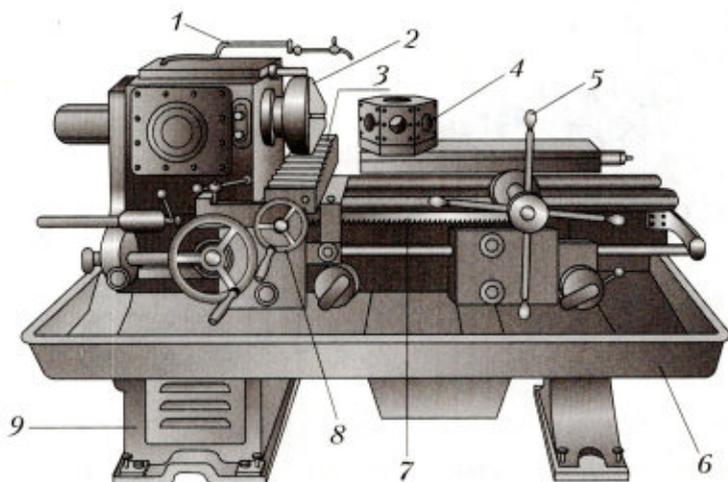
Токарный станок с револьверной головкой первой половины XX века: 1 – подвод смазочно-охлаждающей жидкости; 2 – зажимной патрон; 3 – поперечная каретка; 4 – револьверная головка; 5 – ручной привод перемещения головки; 6 – поддон; 7 – зубчатая рейка механизма продольной подачи; 8 – суппорт; 9 – станина
